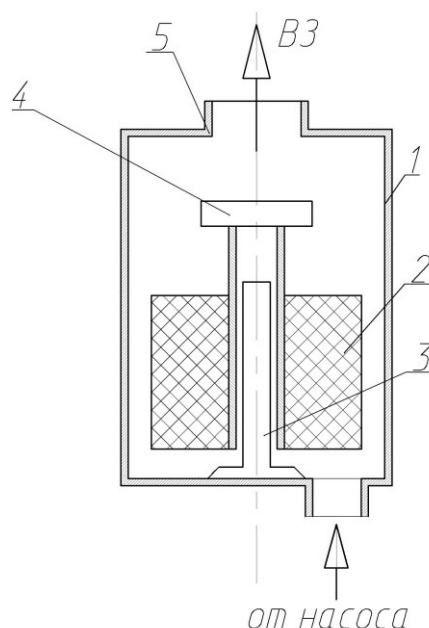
Водоотделитель 1 — корпус; 2 — поплавок; 3 — стержень
